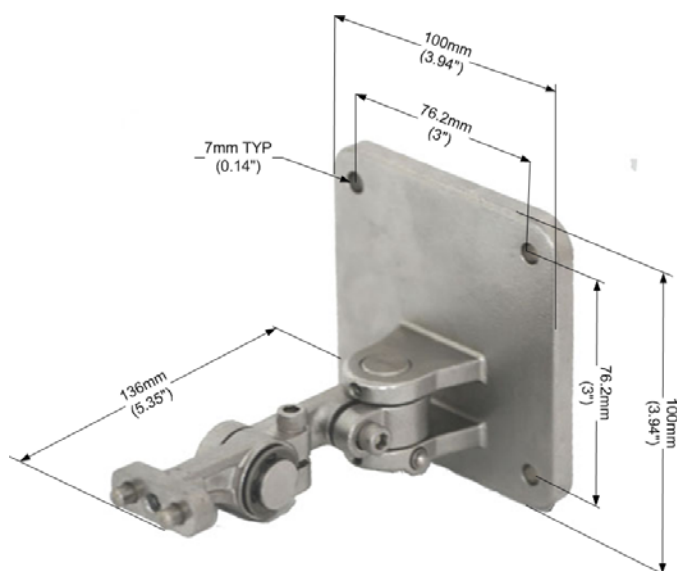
Montage du support pivotant (dimensions en mm et en pouces)
